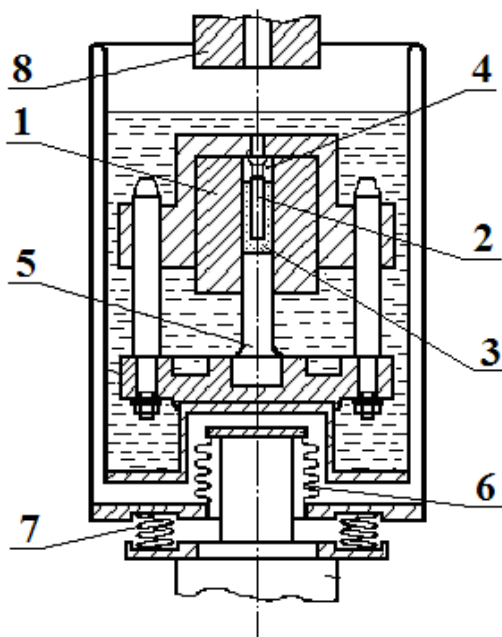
Приставка к прессу для низкотемпературной квазигидроэкструзии. 1-контейнер, 2-заготовка, 3-среда, 4-матрица, 5-пуансон, 6-вставка, 7-пружина, 8-плунжер
